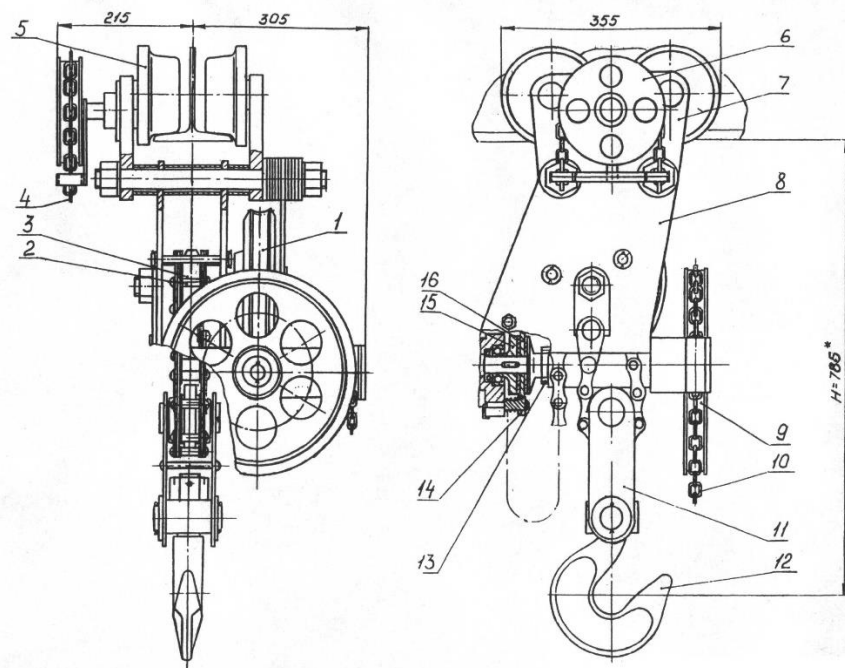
Пристрій ручної талі пересувний черв'ячної
